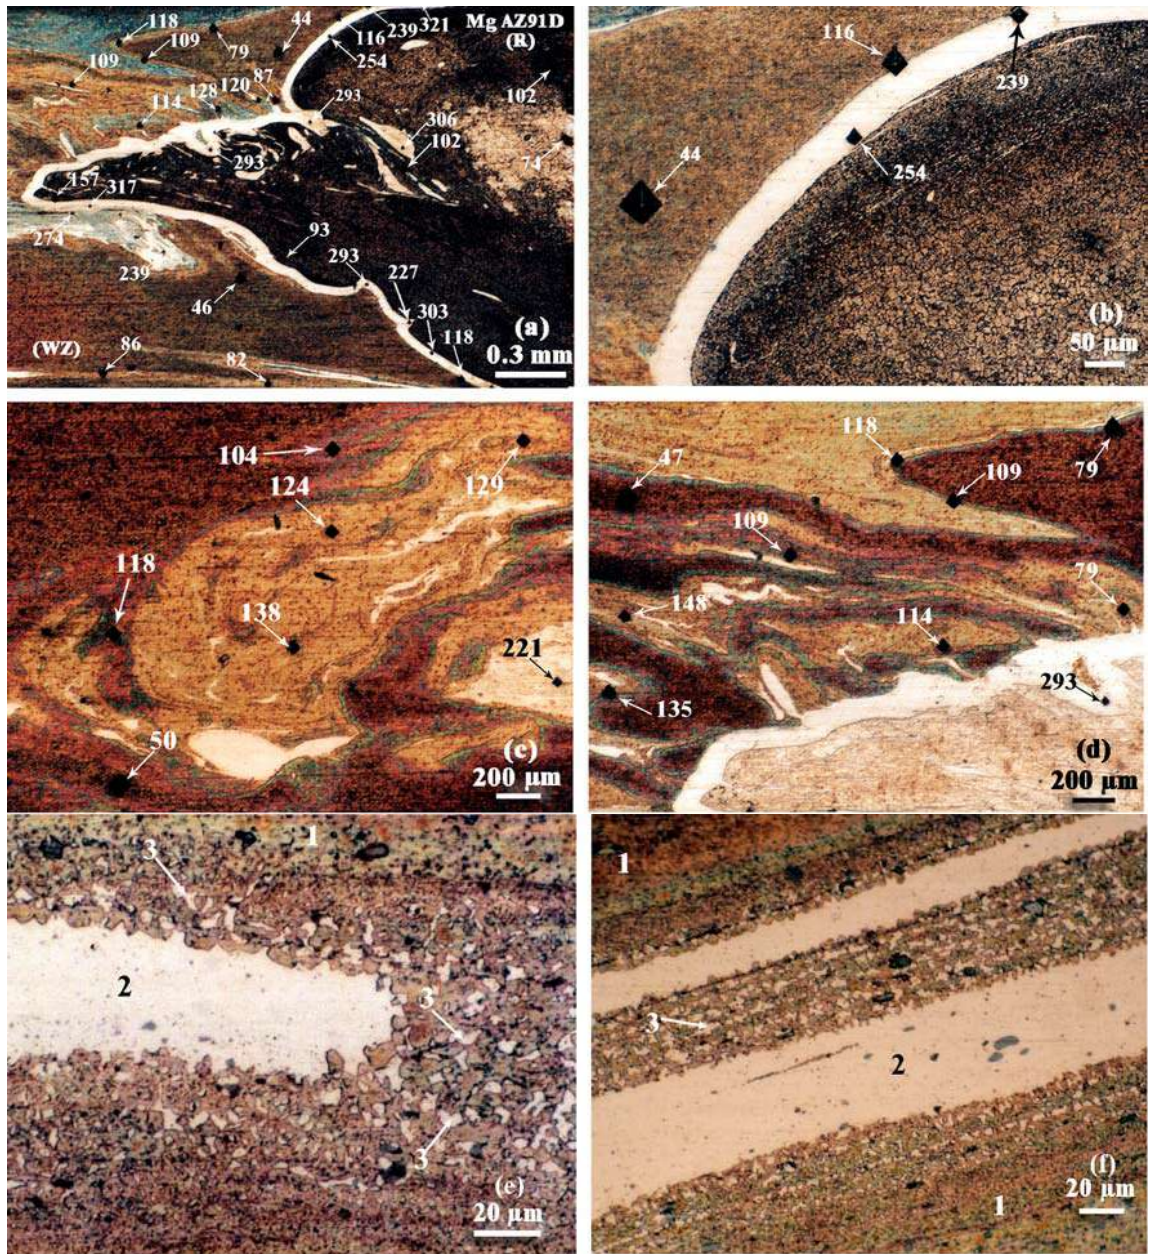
Análisis de la soldadura por fricción realizada sobre una aleación de aluminio 6061-T6 (A) y Mg AZ91D (R). a) Zona de soldadura (WZ) y el lado de retroceso de soldadura (R); b) régimen ampliado de a); c) régimen ampliado de WZ en el lado de avance; d) régimen que muestra la unión de una fase dura y una suave; e) y f) análisis de la unión de Al-Mg: zona de soldadura mostrando la confluencia (zona 3) de los eutécticos e intermetálicos (zona 1) y las áreas más suaves (zona 2) a pesar de la interfaz continua entre ambos. ⁽²⁹⁾
